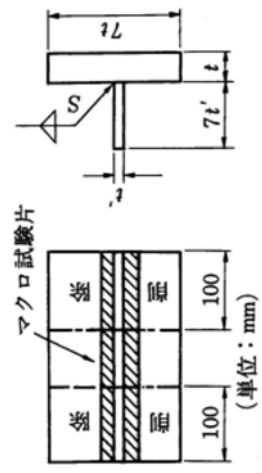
すみ肉溶接試験（マクロ試験） 溶接方法及び試験片の形状
